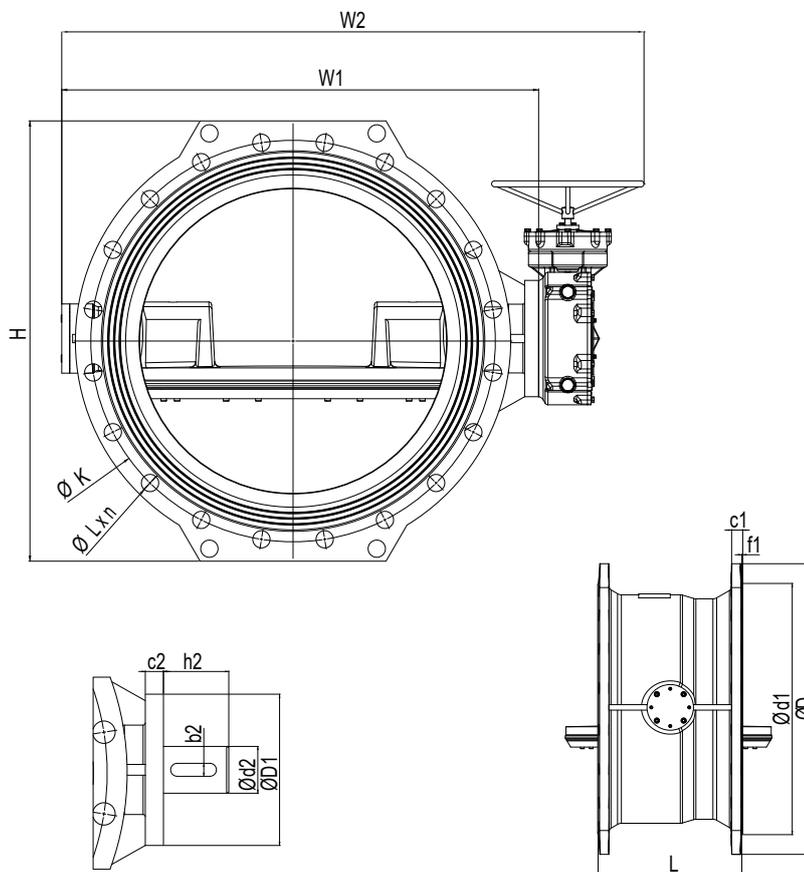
Disegno di sezione PN N10 DN 1200 - 2200
